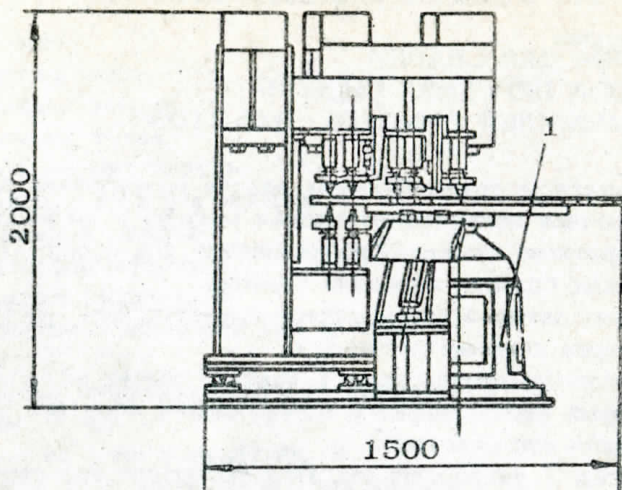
Машина для сварки салазок передних сидений автомобиля.
